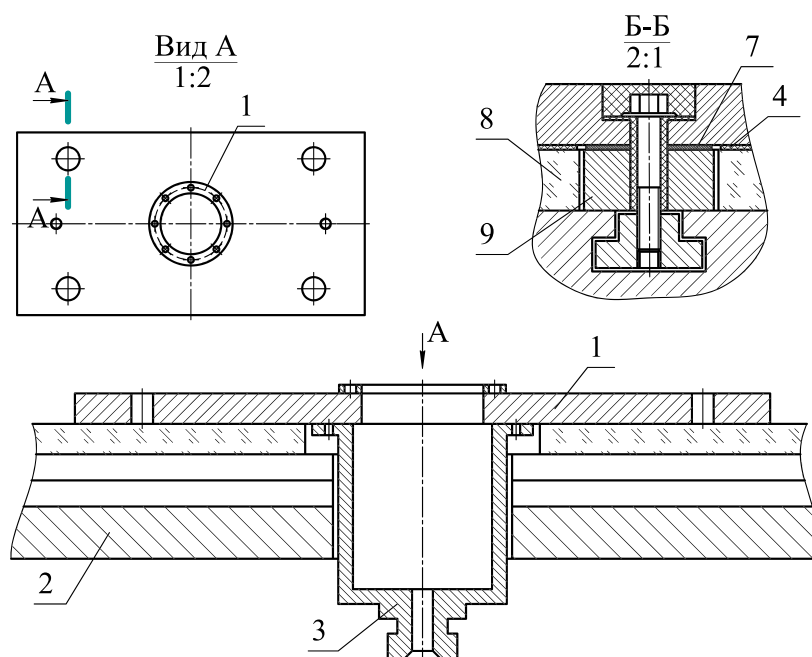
Плита для установки, базирования и закрепления приспособлений: 1 – плита; 2 – стол; 3 – патрубок подвода электролита; 4 – масса; 5 – эпоксидный клей; 6 – винты; 7 – изоляционные прокладки; 8 – дно камеры; 9 – промежуточные опоры.
